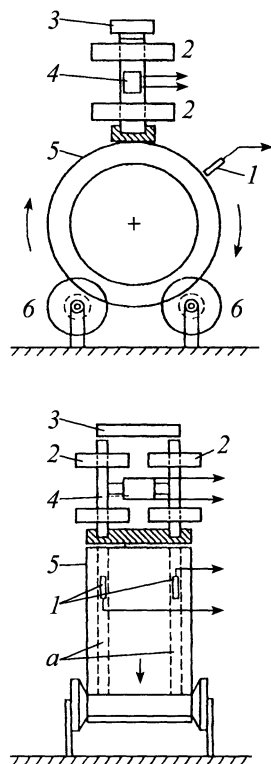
Устройство для магнитного контроля подшипниковых колец большого размера
